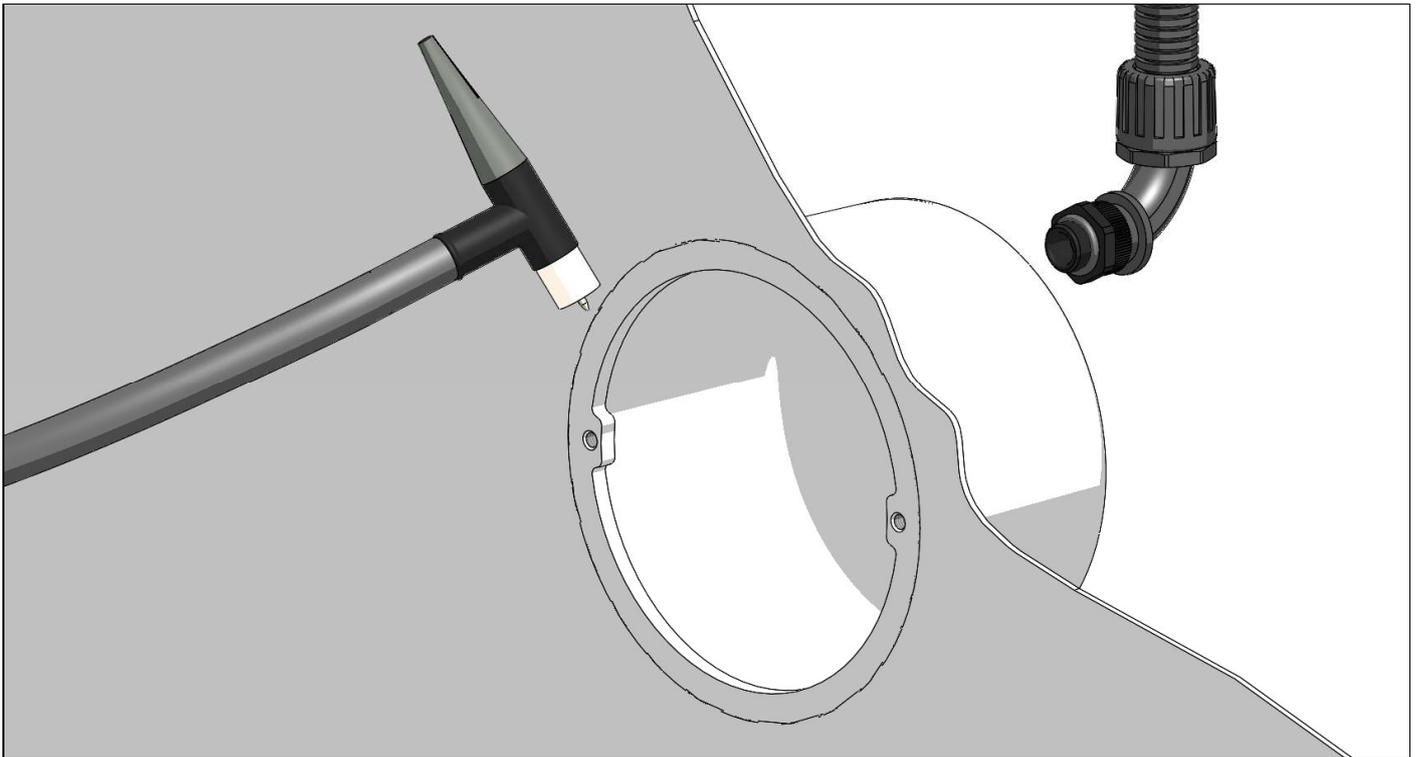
Einbaugehäuse Edelstahlbecken – beckenbündig einschweißen (Kabelschutzsystem anschließend dicht montieren)
